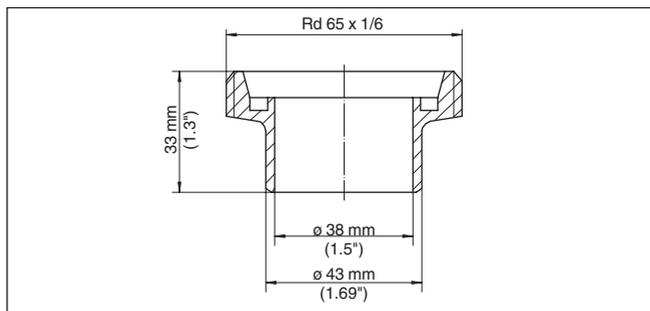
Medidas da luva para soldagem união roscada para tubo DN 40
